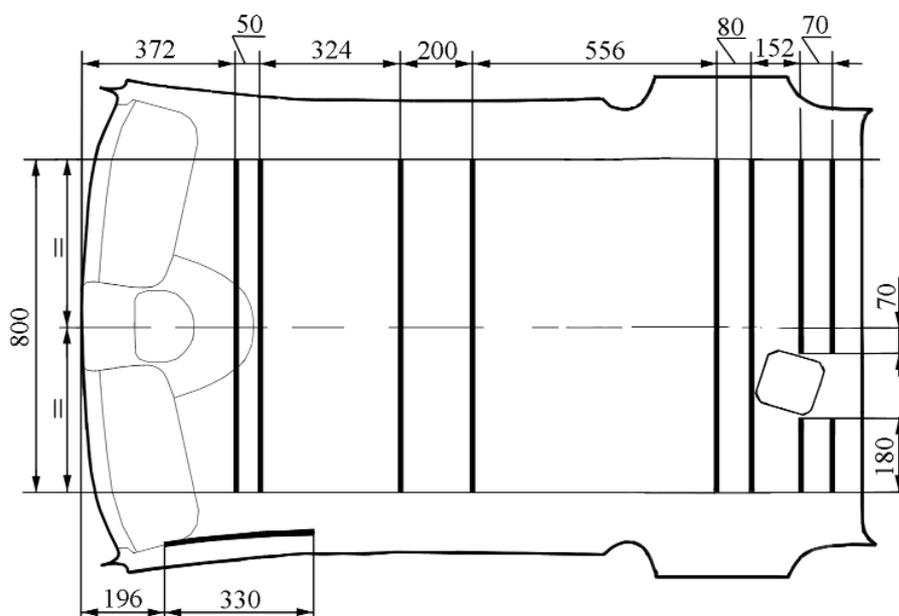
Схема нанесения клея на обивку крыши.
